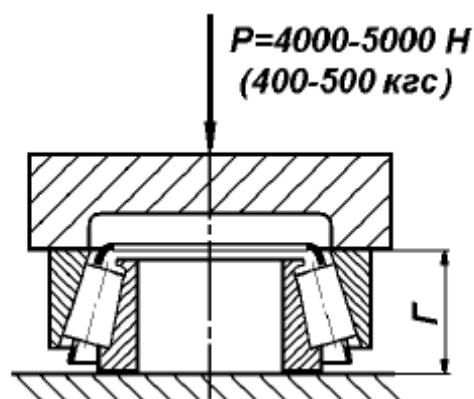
Замер монтажной высоты подшипника ведущей шестерни
